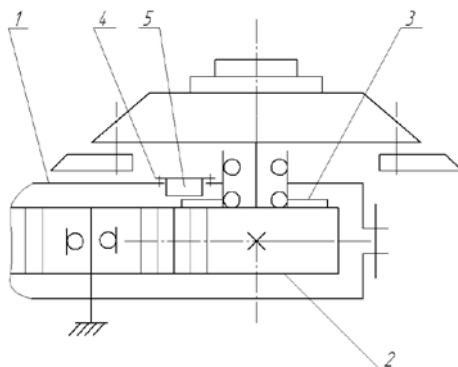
Режущий аппарат с магнитами: 1 – крышка редуктора; 2 – шестерня с цилиндрической вставкой; 3 – цилиндрическая вставка; 4 – крышка; 5 – магнит
